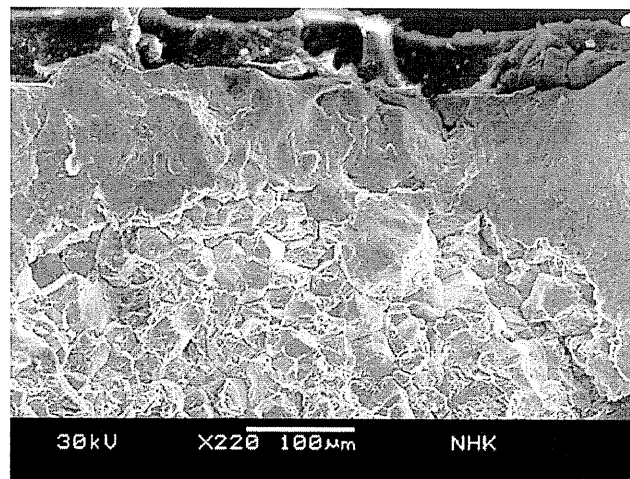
淬火裂縫導致的晶粒間破裂面(intergranular fracture surface)[46]
